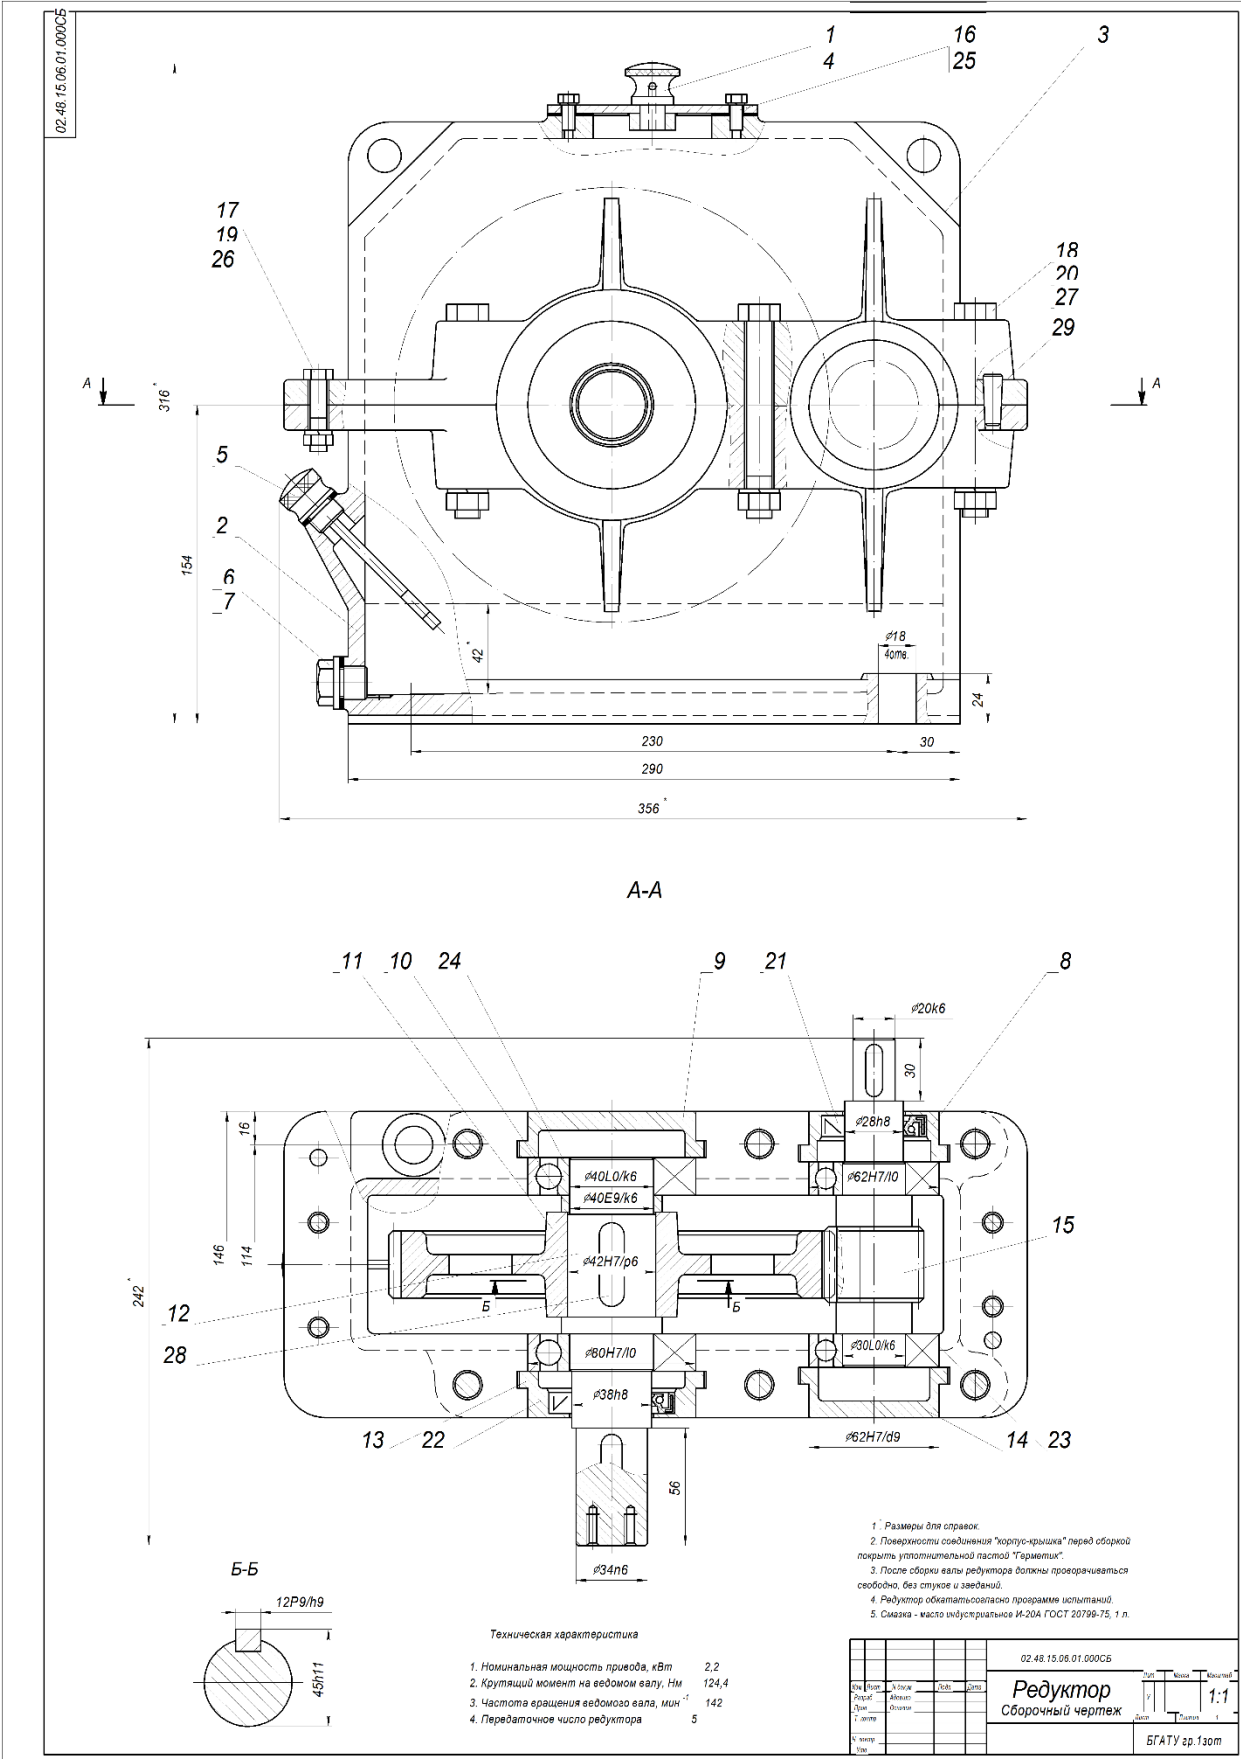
Редуктор цилиндрический одноступенчатый горизонтальный с вертикальным валом (разрез по осям валов)
